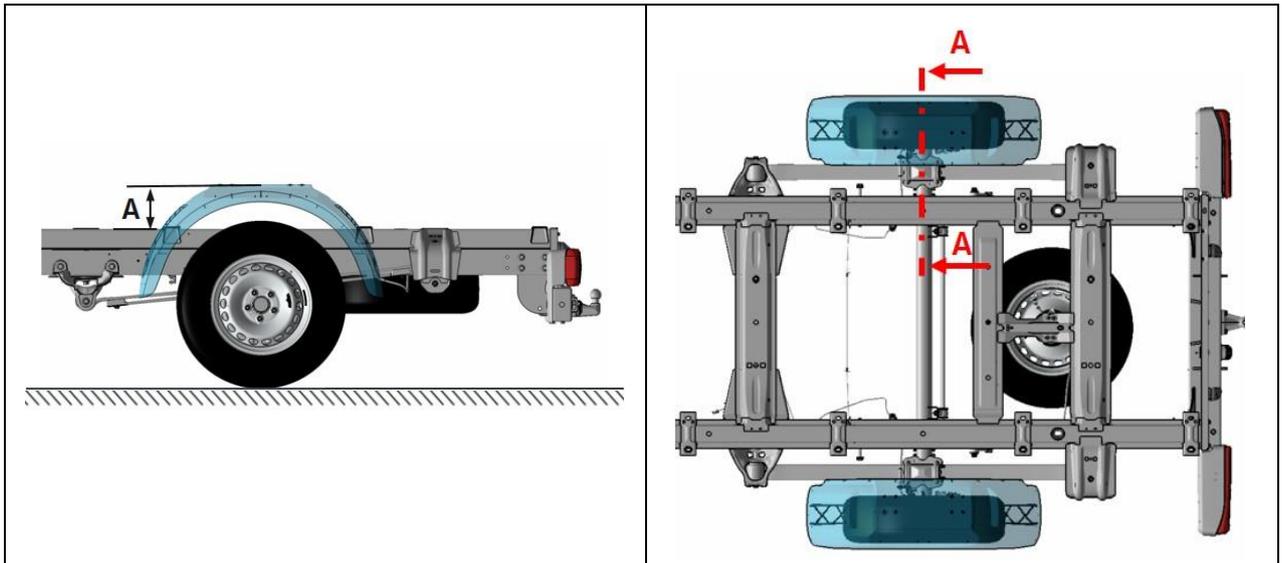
Dimensions passage de roue / cache partiel (exemple : passage de roue plateau de série)
